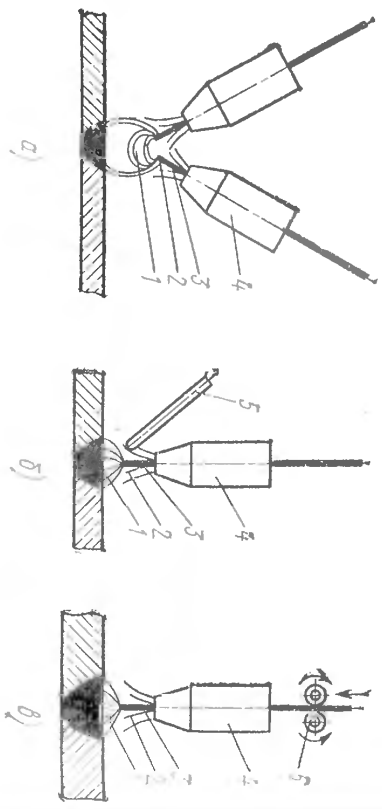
Способы дуговой сварки в защитном газе:
